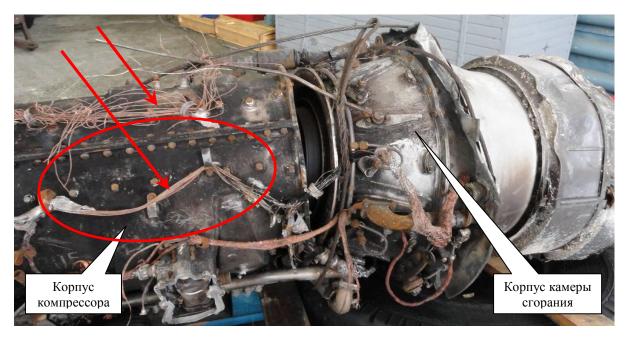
Общий вид верхней части корпуса двигателя в состоянии поступления на исследование.
